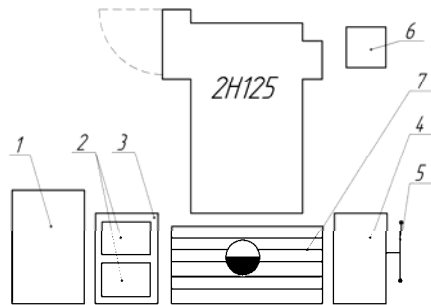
Организация рабочего места сверловщика где: 1 – стеллаж-подставка; 2 – тара; 3 – столик приёмный; 4 – тумбочка инструментальная двухсекционная; 5 – планшет для чертежей; 6 – стеллаж для приспособлений; 7 – решетка под ноги
